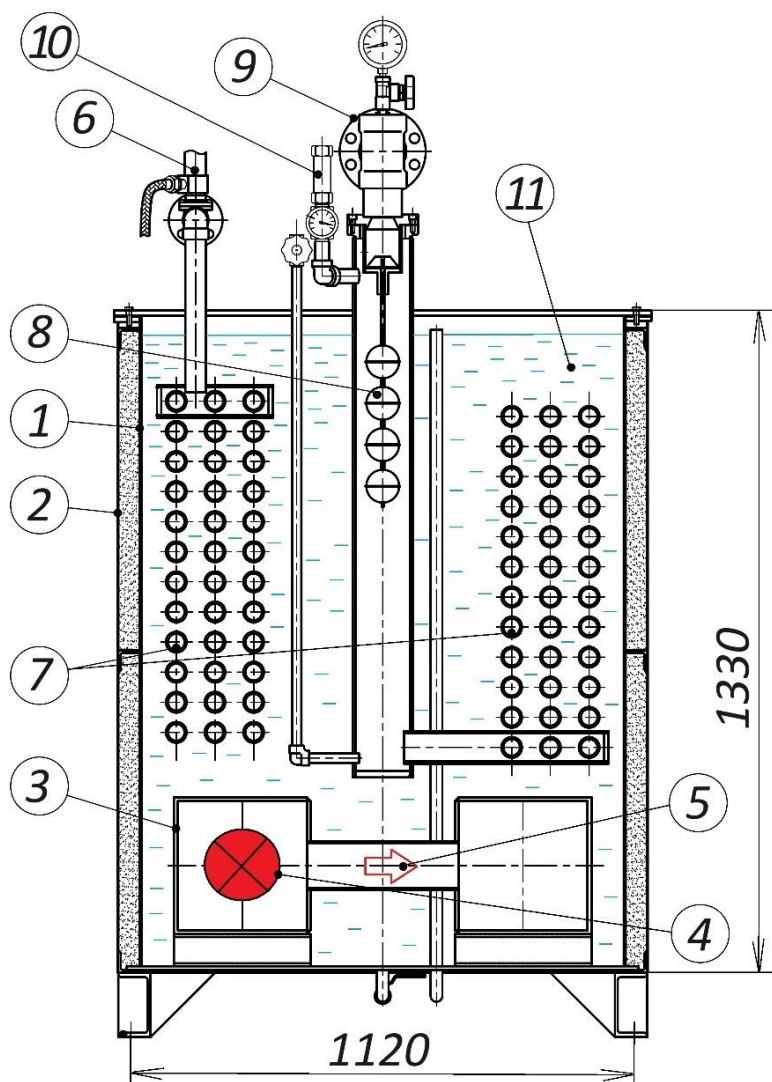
Принципова конструкція випарника 1000 кг/год по пропан-бутану: 1 – металевий корпус випарника; 2 – зовнішня ізоляція; 3 – камера згорання; 4 – газовий факел; 5 – відведення димових газів; 6 – подача рідкого
